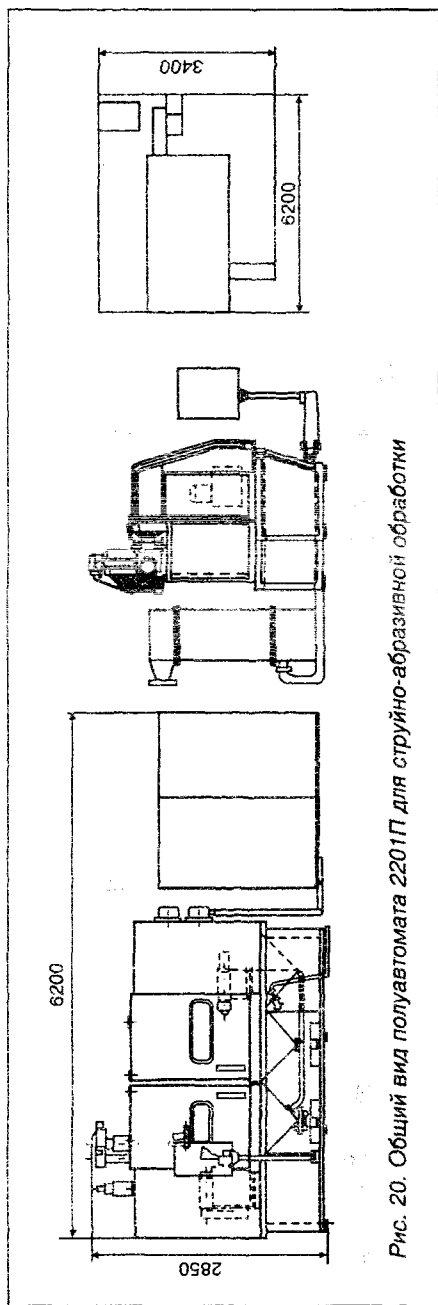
Общий вид полуавтомата 2201П для струйно-абразивной обработки
